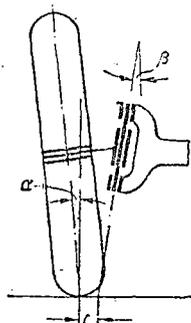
Схема развала колеса и поперечного наклона шкворня:
